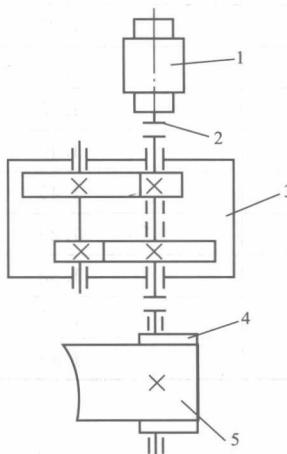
二级同轴式斜齿圆柱齿轮减速器设计
